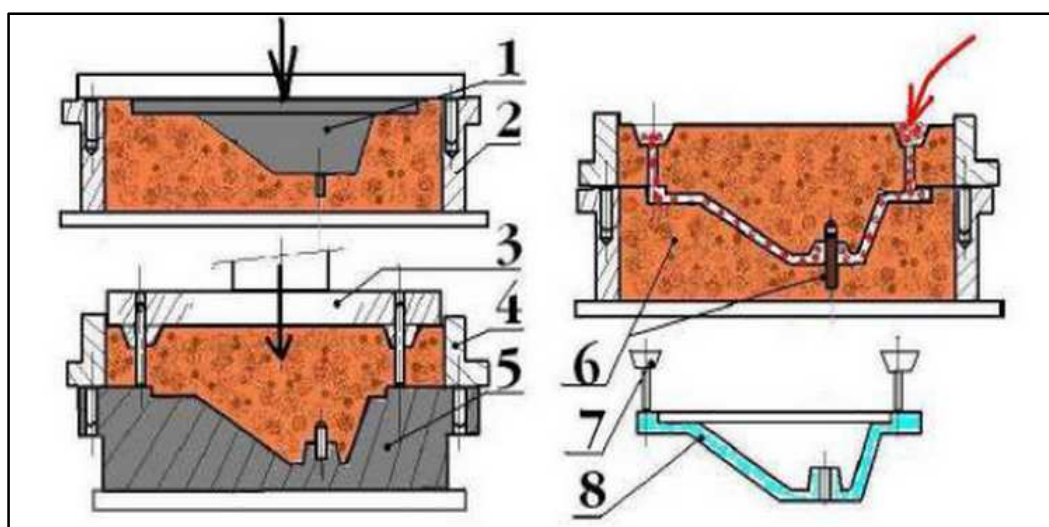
Exemple d'obtention d'une pièce par moulage en sable à joint horizontal.
